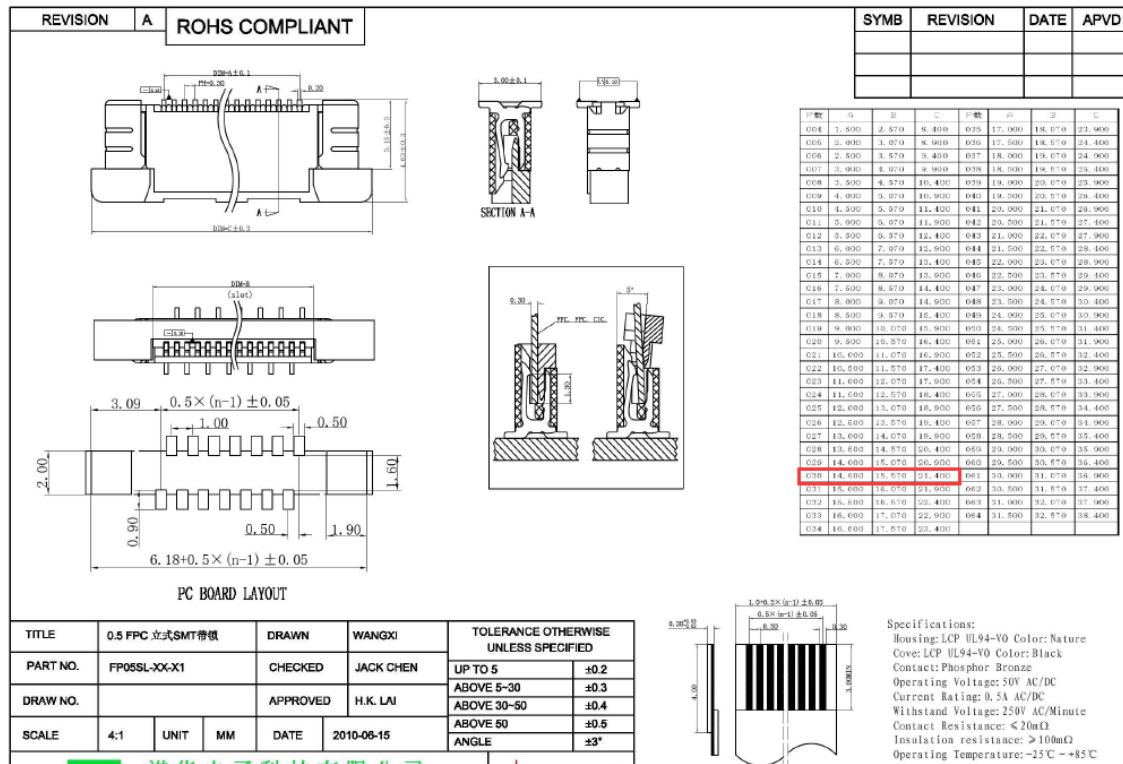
间距 0.5mm 立式双排 30 PIN PCB 封装
